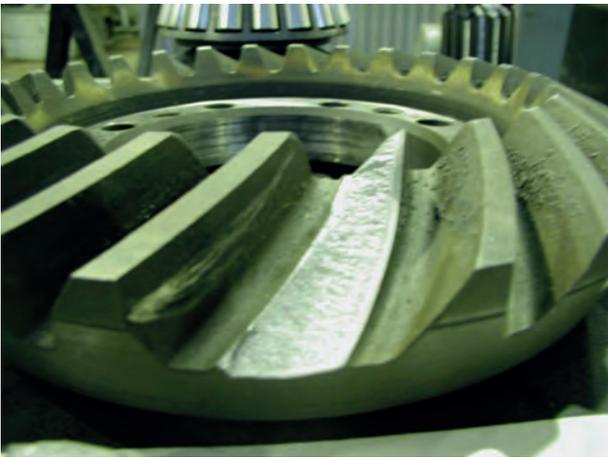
Пример разрушения зуба шестерни при статических испытаниях (в большинстве случаев при одинаковой нагрузке в первую очередь ломался зуб не чугунной, а стальной шестерни)
